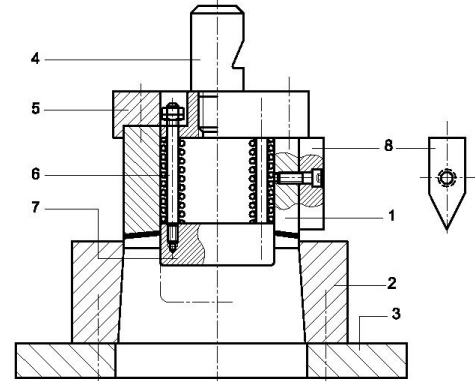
Beschneidwerkzeug - Abfalltrenner
